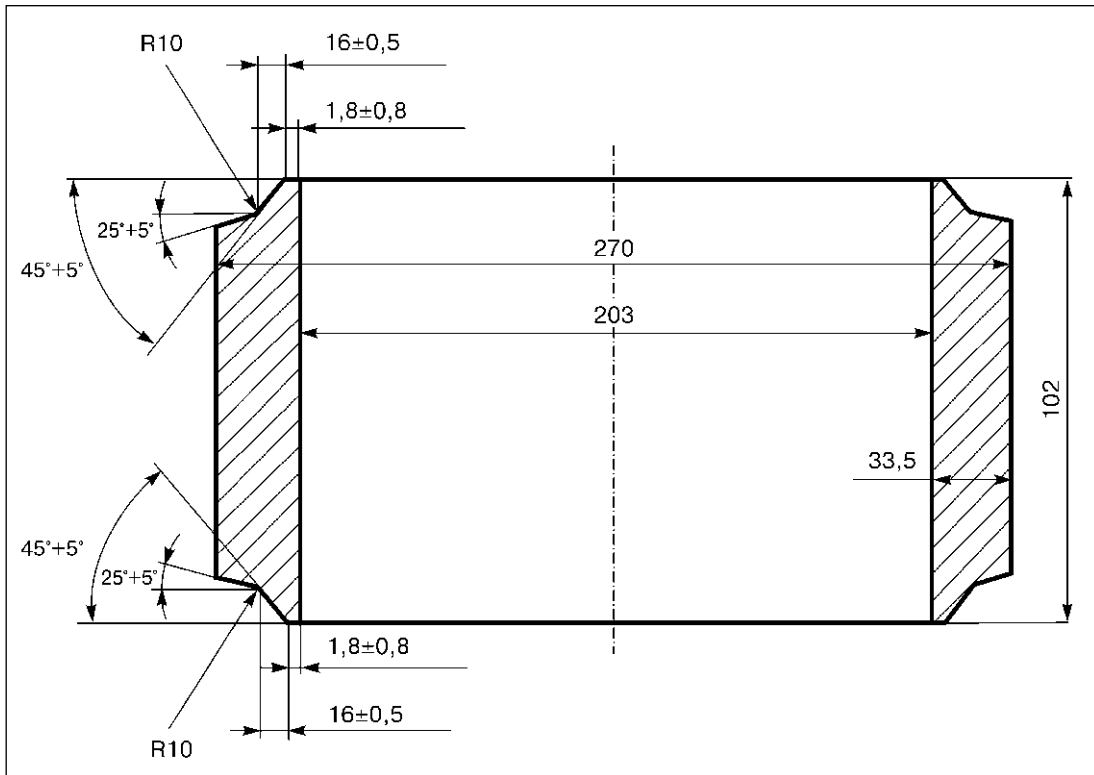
Новый ремонтный патрубок со сточенными фасками под сварку с днищем и фланцем
